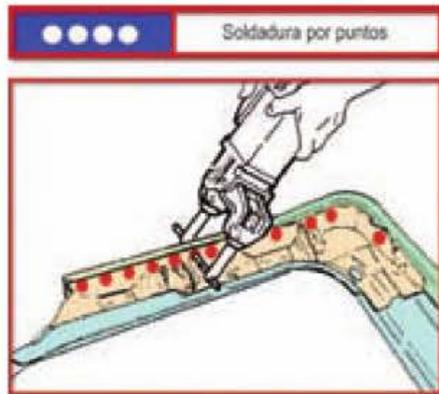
Pictograma de soldadura por puntos.
